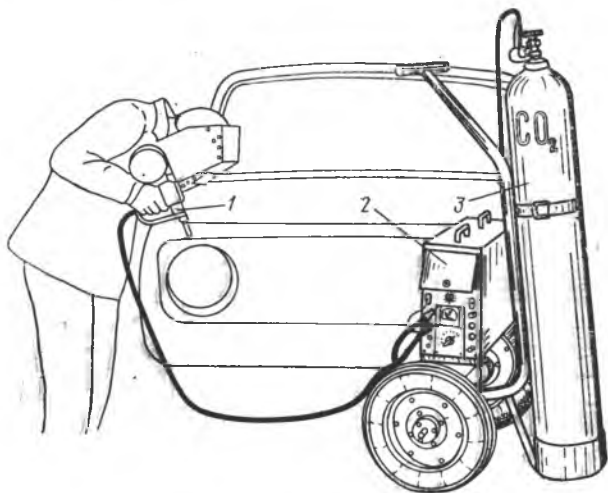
Общий вид передвижной полуавтоматической установки И-103 «Луч»:
